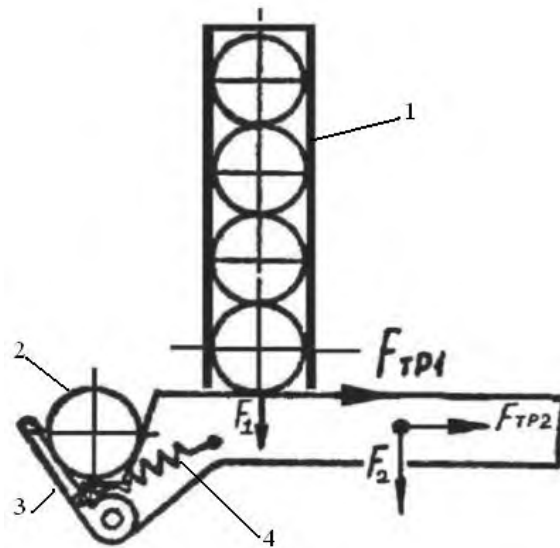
Схема механизма поштучной выдачи: 1 – лоток-магазин; 2 – изделие; 3 – рычаг; 4 – пружина растяжения
